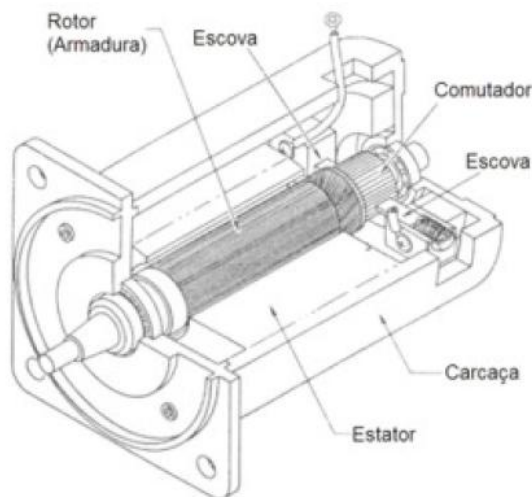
Motor elétrico de corrente contínua com seus principais componentes.
